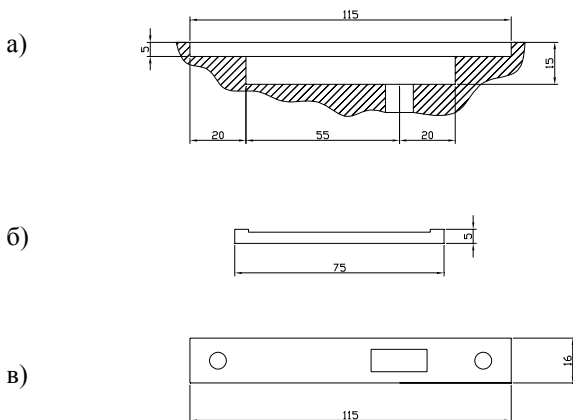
Общий вид узла крепления образца (а); планка 1(б); планка 2 (в)
